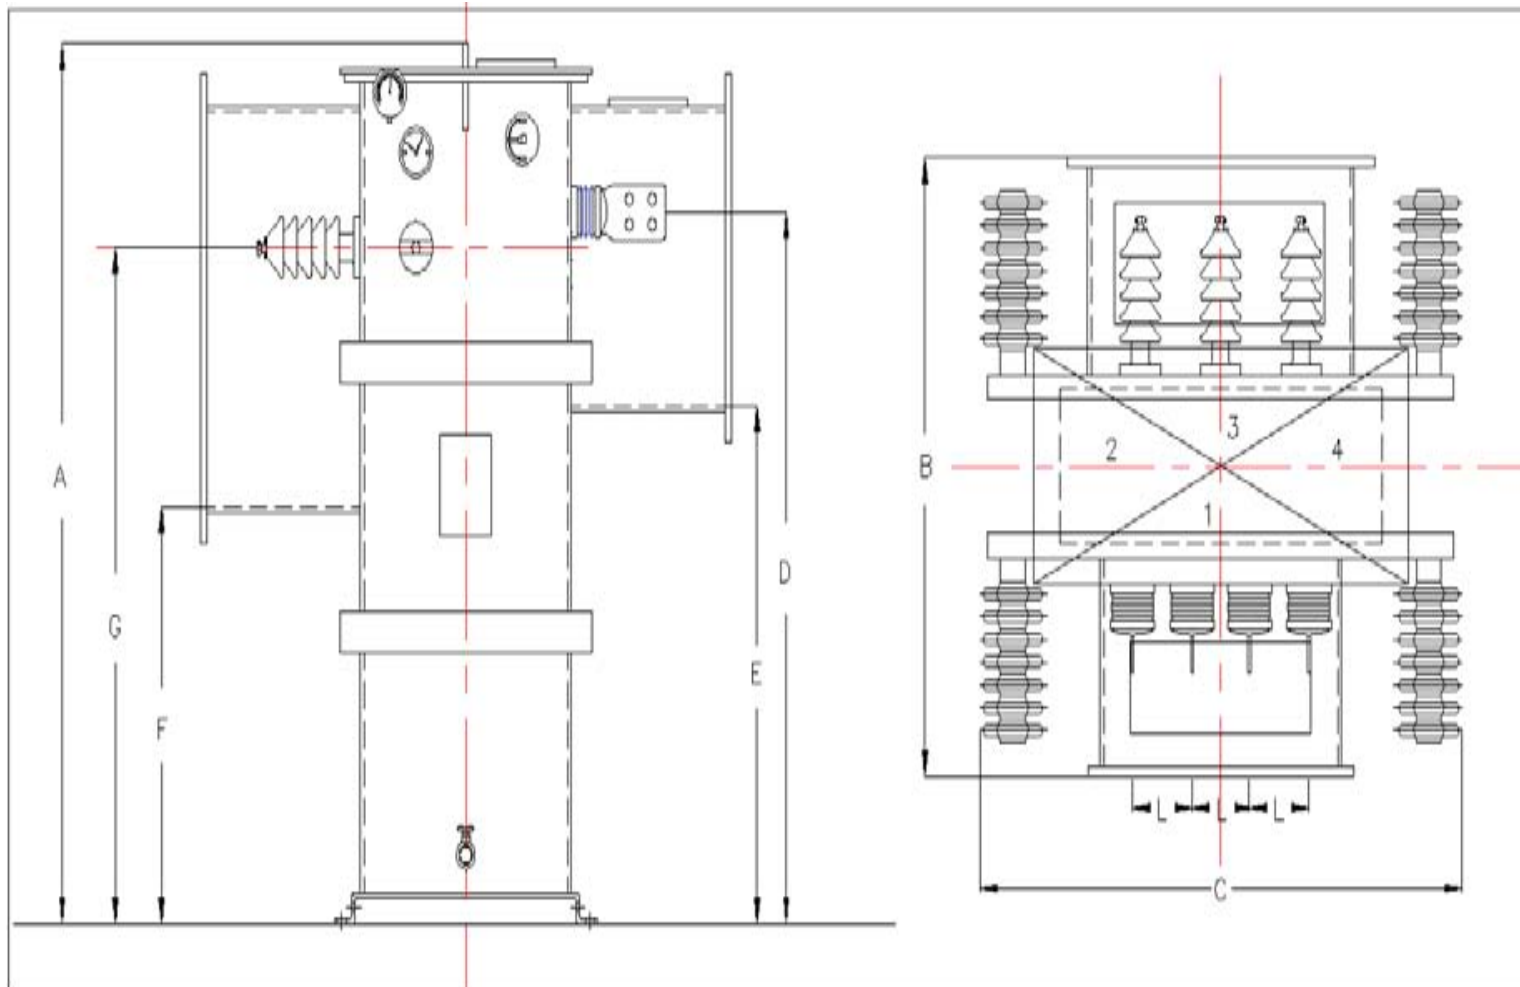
DIMENSIONES DE UN TRANSFORMADOR
